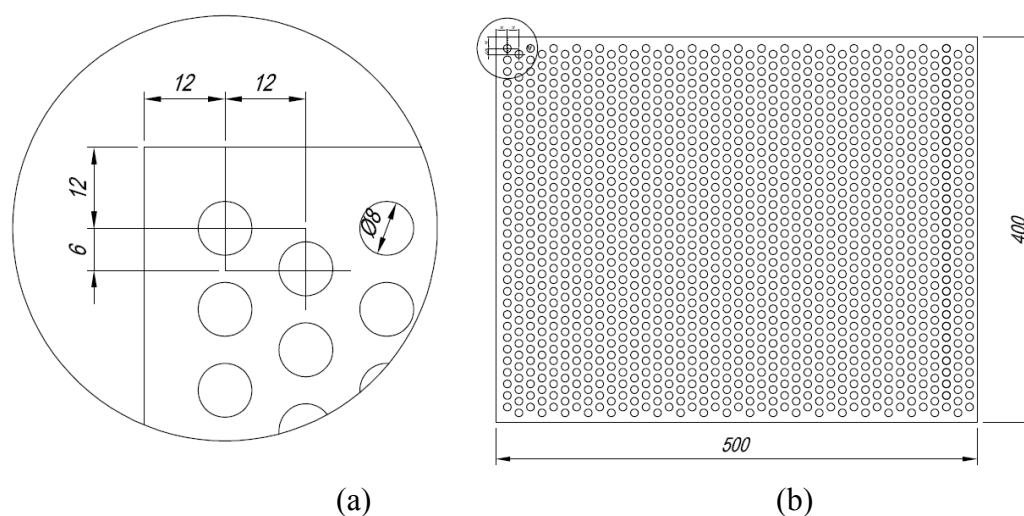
Desenho das placas após furação (a) dimensões das margens e (b) dimensão das placas
